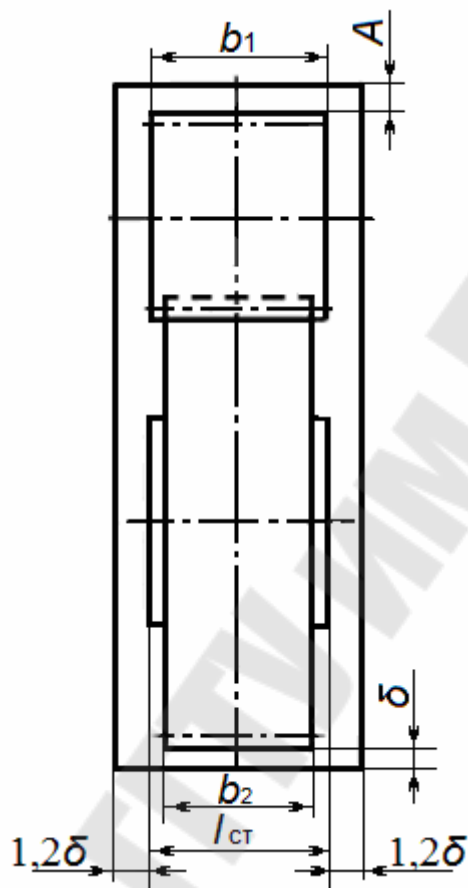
Схема расположения зубчатого зацепления в внутри корпуса редуктора
